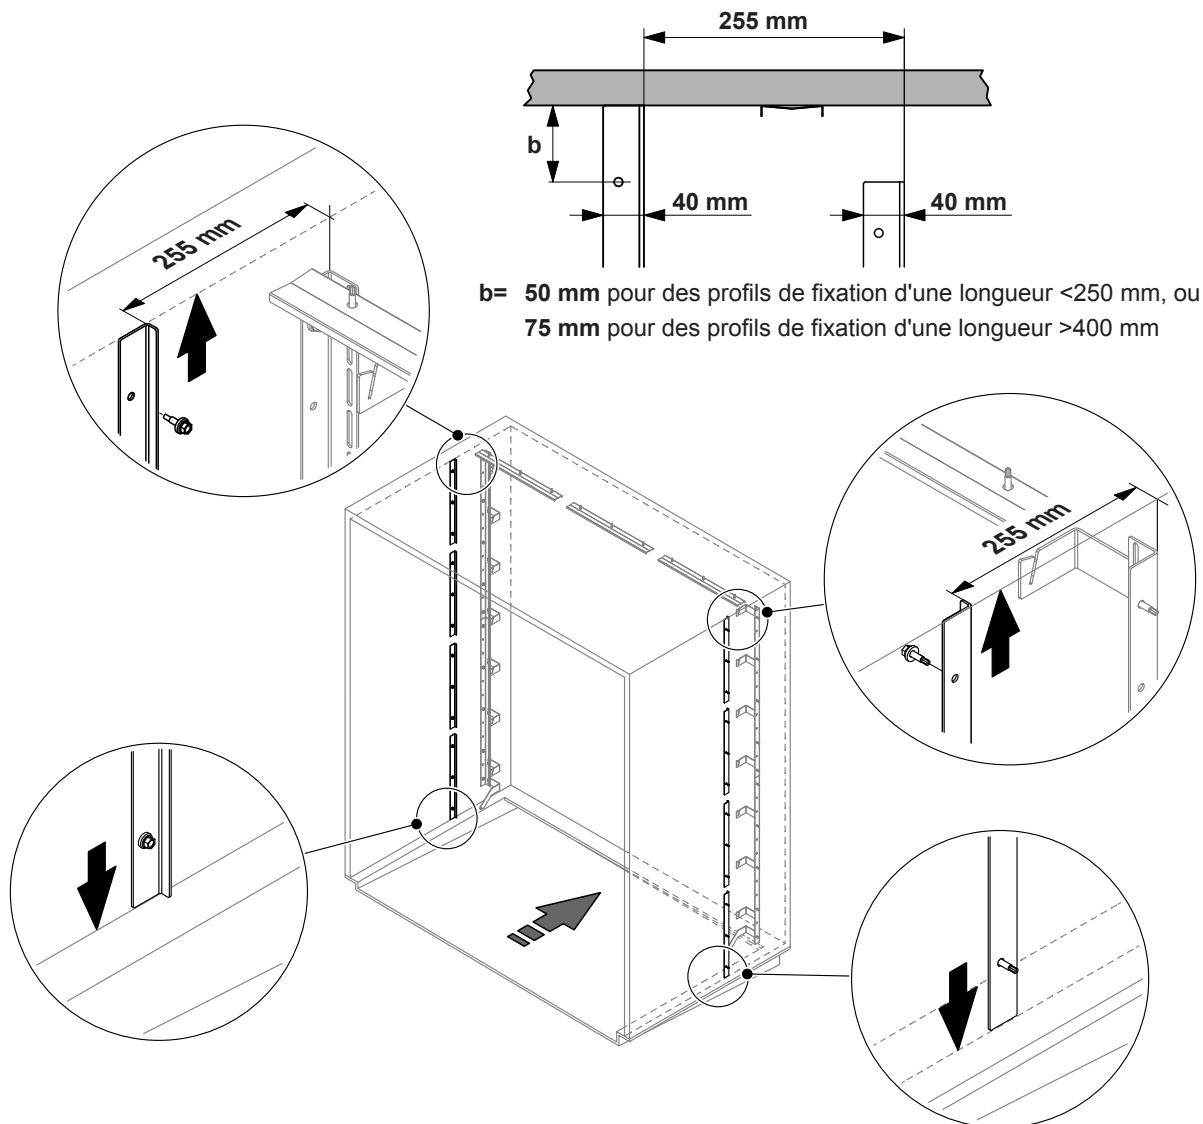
Montage des profils de fixation pour les tôles d'étanchéité latérales
